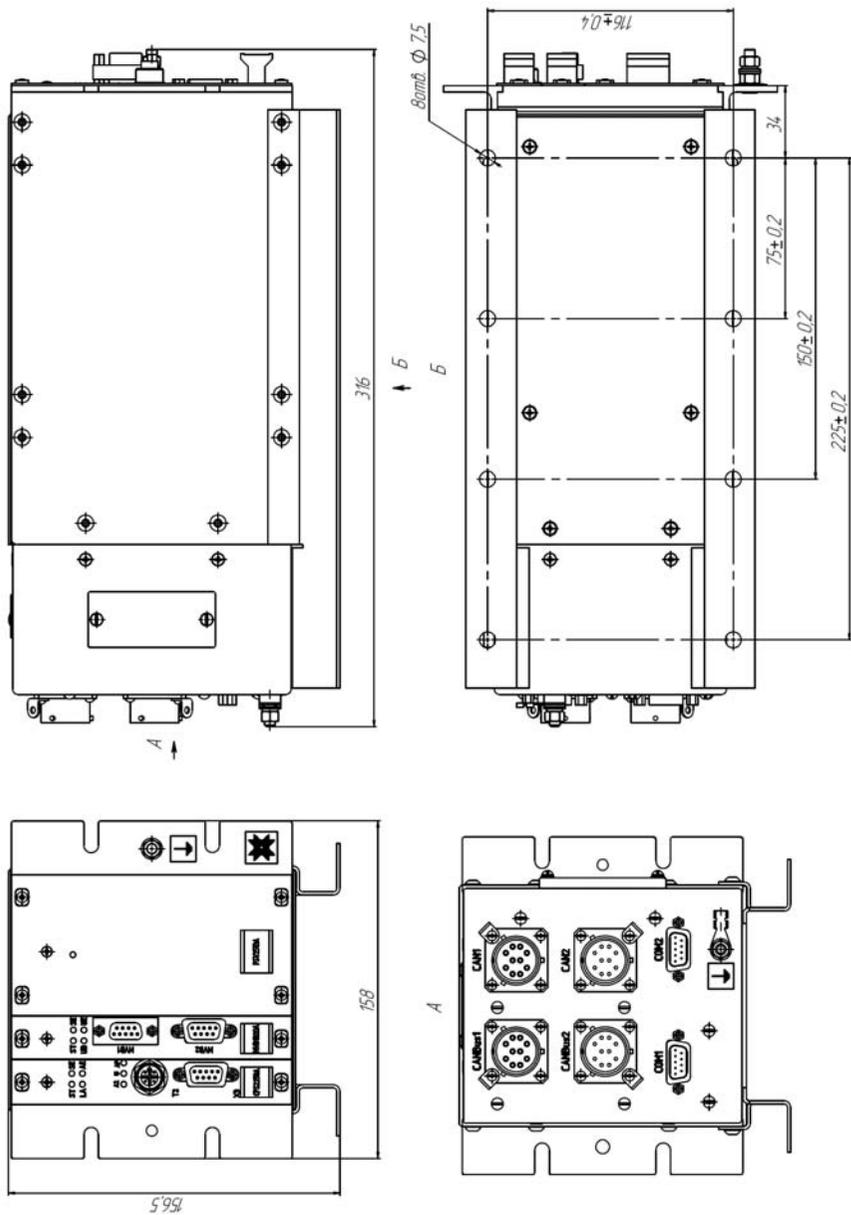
Внешний вид, габаритные и установочные размеры изделия
